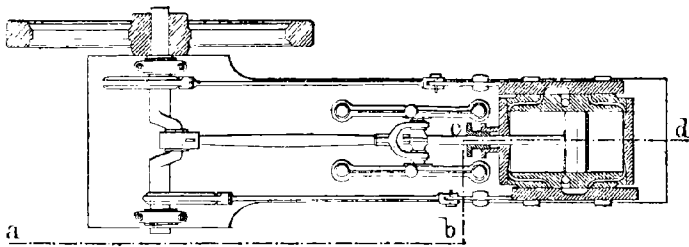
Moteur à gaz Lenoir (coupe horizontale).
